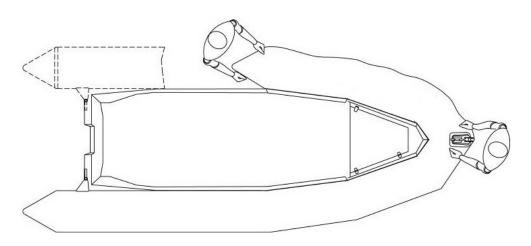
MONTAGE DU FLOTTEUR 3 FIGURE 3.1.1.2.3 – TUBE INSTALLATION 3
